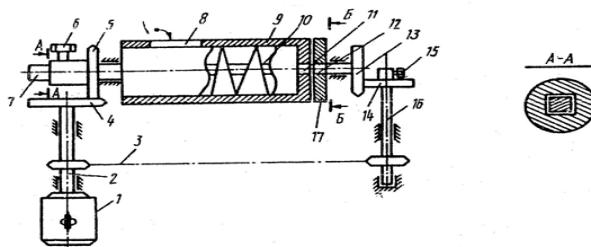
Схема передаточного механизма, устройство для формования полуфабрикатов кондитерских изделий
